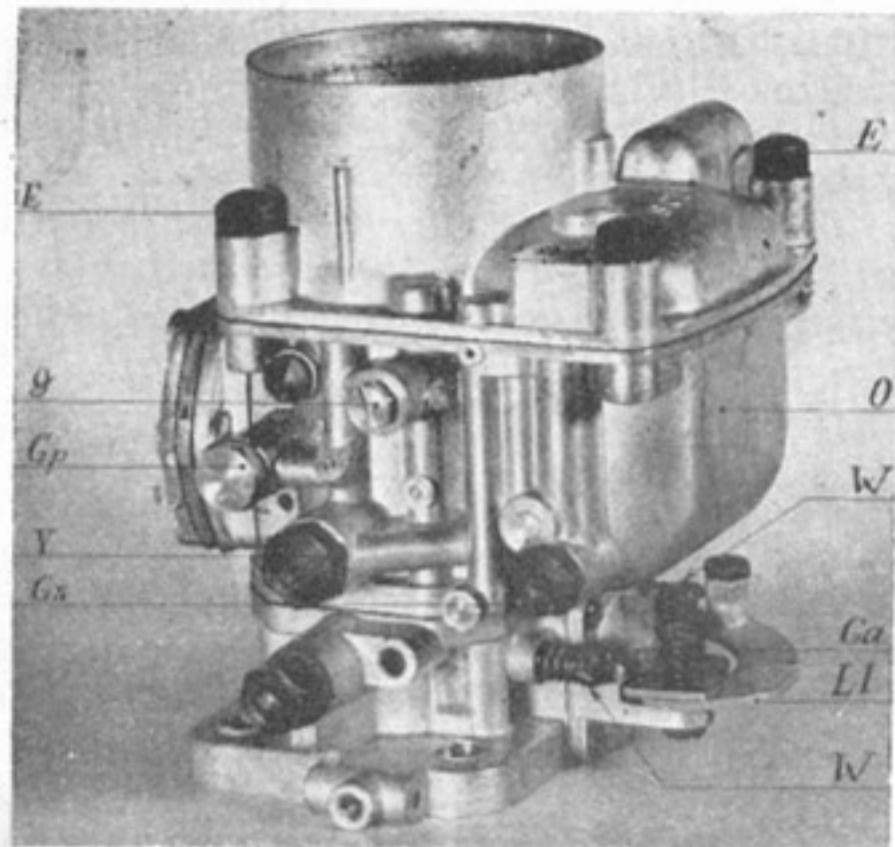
Schema karburátoru MOTORPAL-SOLEX 30 UAAIP:
